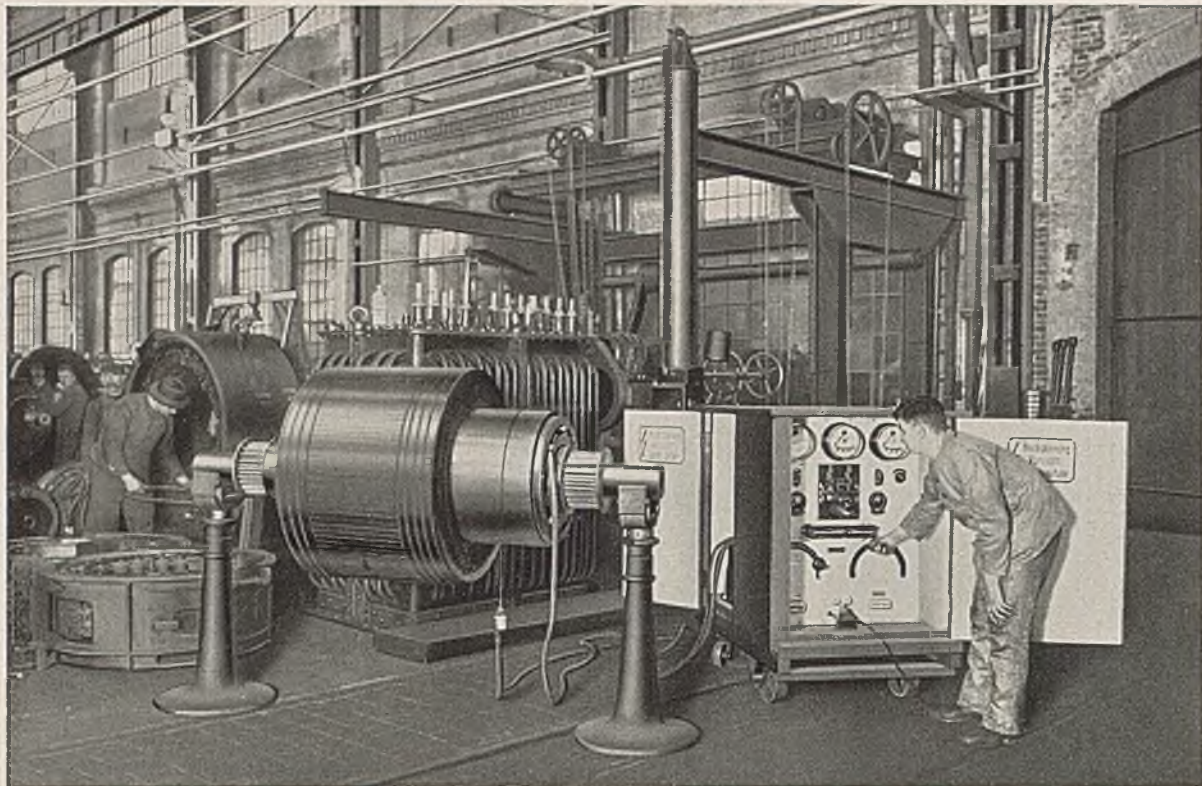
Fahrbare Hochspannungs-Prüfeinrichtung für elektrische Maschinen.
